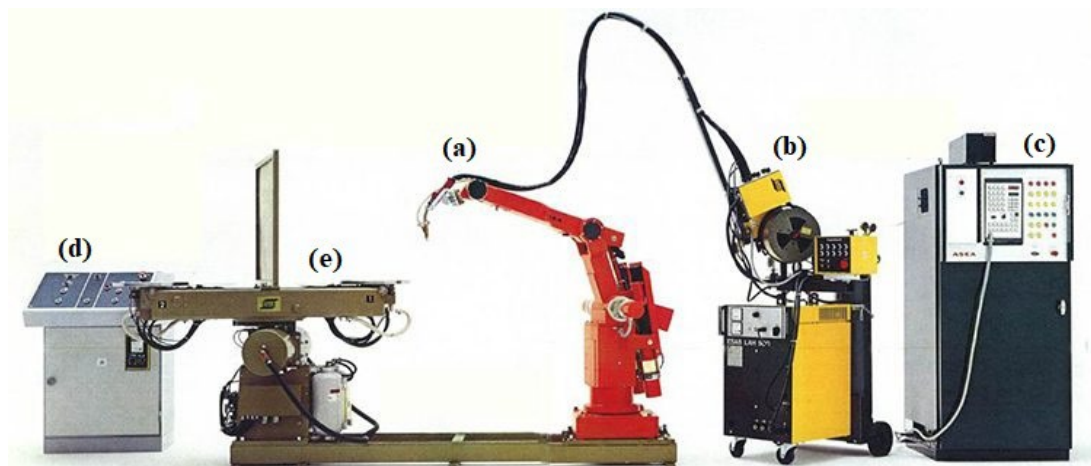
Célula de soldagem com robô industrial, formada por (a) um braço robótico articulado ASEA IRB 6, (b) uma máquina de solda, (c) uma caixa de controle, (d) um painel de operação, e (e) um posicionador [6].
